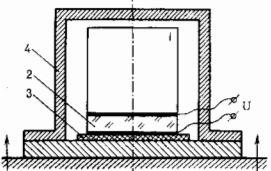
Пьезоприёмник ускорения: 1 — пьезоэлемент; 2 — инертная масса; 3 — упругая прокладка; 4 — корпус.
